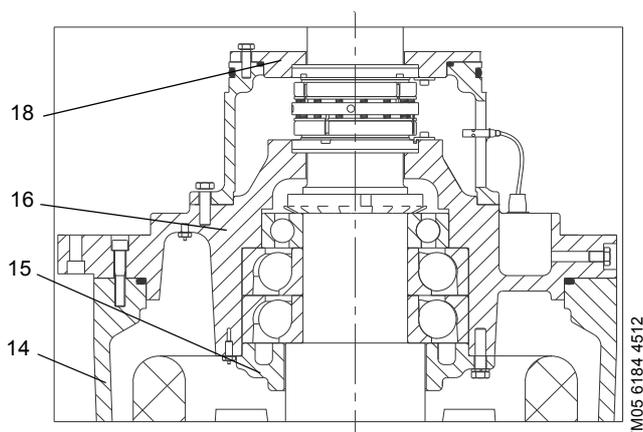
Детали уплотнения и подшипника, KPL 1000-1800
